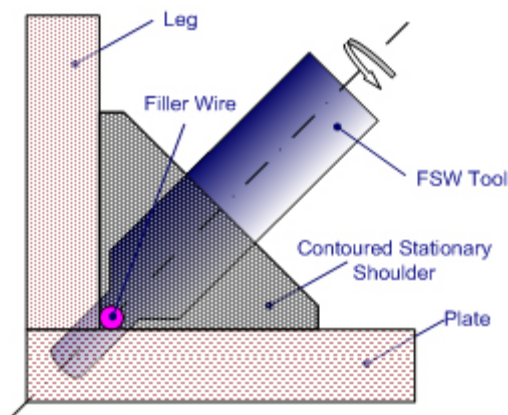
Schéma du cordon de soudure d'angle AdStir SSFSW [29]
